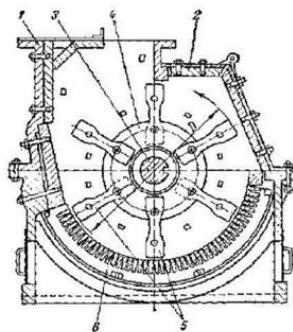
Схема молотковой дробилки: 1 – корпус; 2 – отбойная плита; 3 – вал; 4 – диск; 5 – молотки; 6 – колосниковая решетка.
